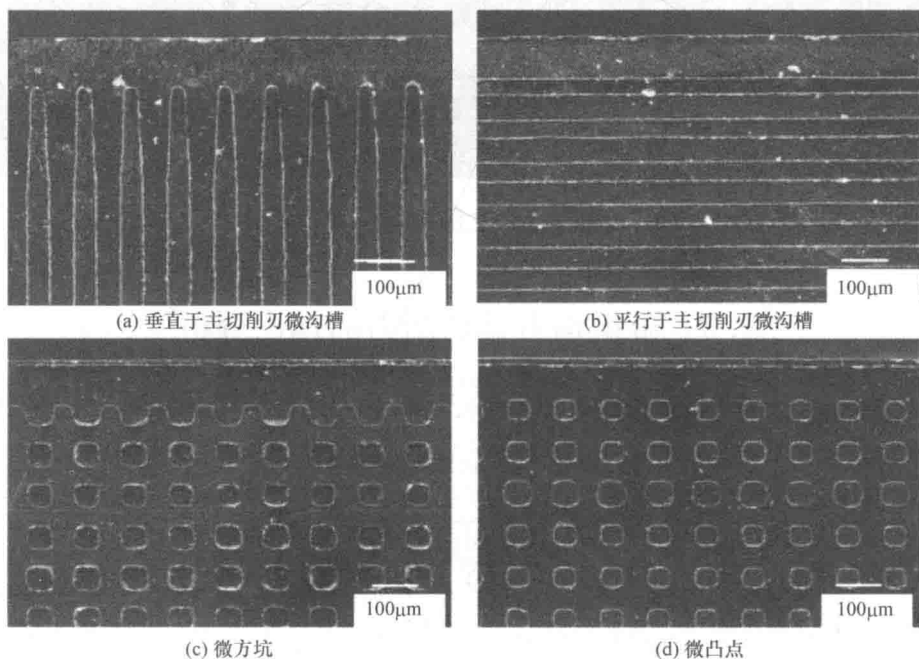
PCBN 刀具表面电火花加工的微结构形貌
